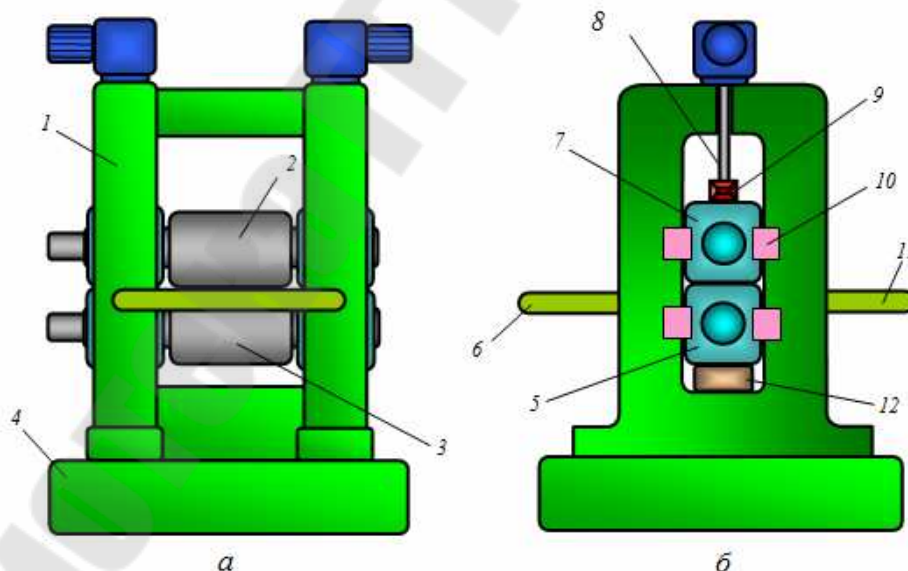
Рабочая клетка: *а* — вид спереди; *б* — вид сбоку; 1 — станина; 2, 3 — верхний и нижний рабочие валки; 4 — плитовина; 5, 7 — нижняя и верхняя подушки; 6, 11 — входной и выходной столы с линейками для монтажа привалкой арматуры; 8 — нажимное устройство; 9 — предохранительное устройство; 10 — устройство осевой установки и фиксации валков; 12 — устройство установки нижнего валка
